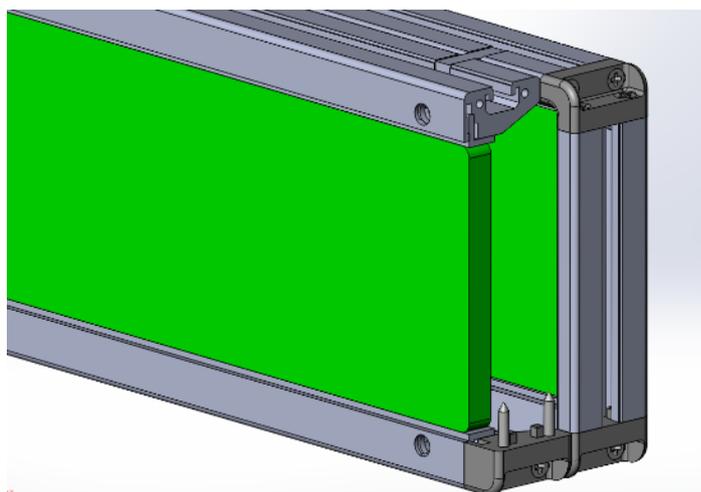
Каркас с установленными дисплейными модулями. Скрыт угловой соединитель и рамочный профиль
